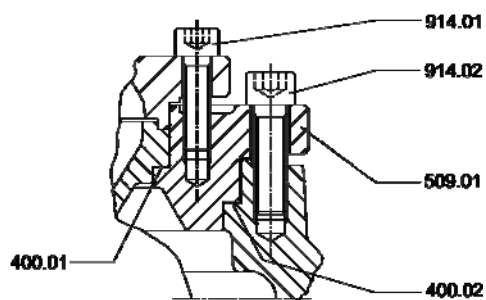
Исполнение с кольцевой прокладкой, типоразмеры 40-250/01 и 50-250/01
